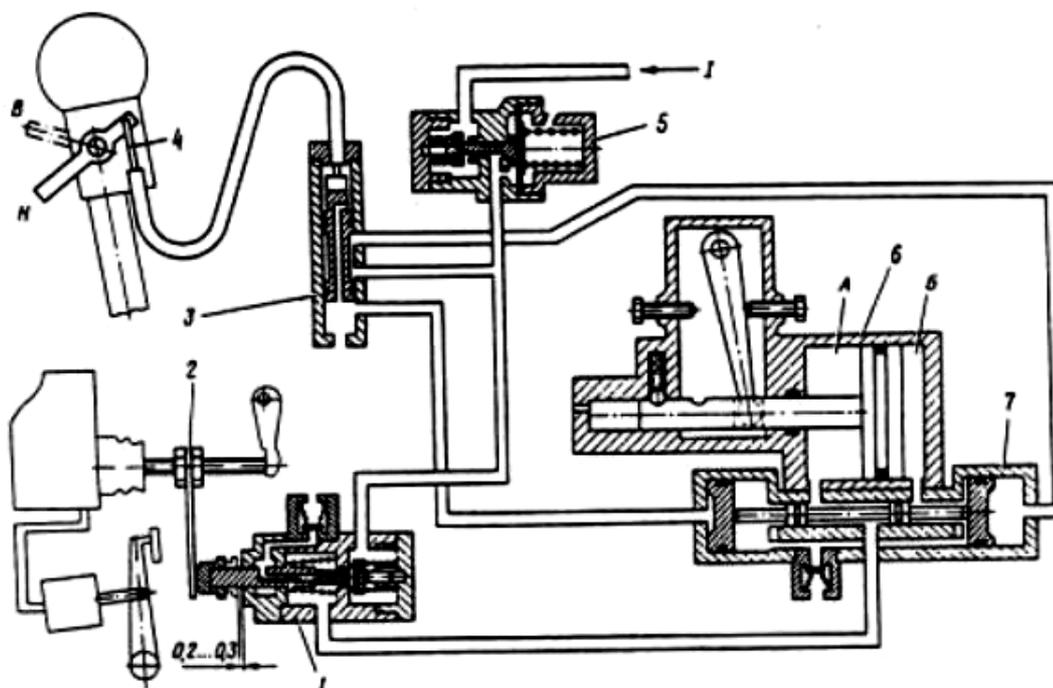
Пневматическая система управления делителем передач: I — воздух из пневмопривода тормозов; Н, В — низшая и высшая передачи в делителе; 1 — клапан включения делителя; 2 — упор штока клапана; 3 — кран управления; 4 — трос; 5 — редукционный клапан; 6 — механизм переключения передач; 7 — воздухораспределитель
